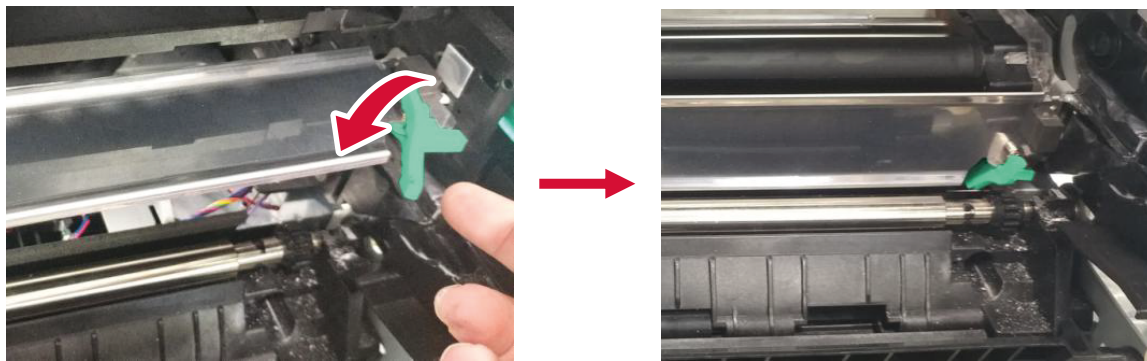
Установка блока проявки в корпус МФУ «Гравитон»
